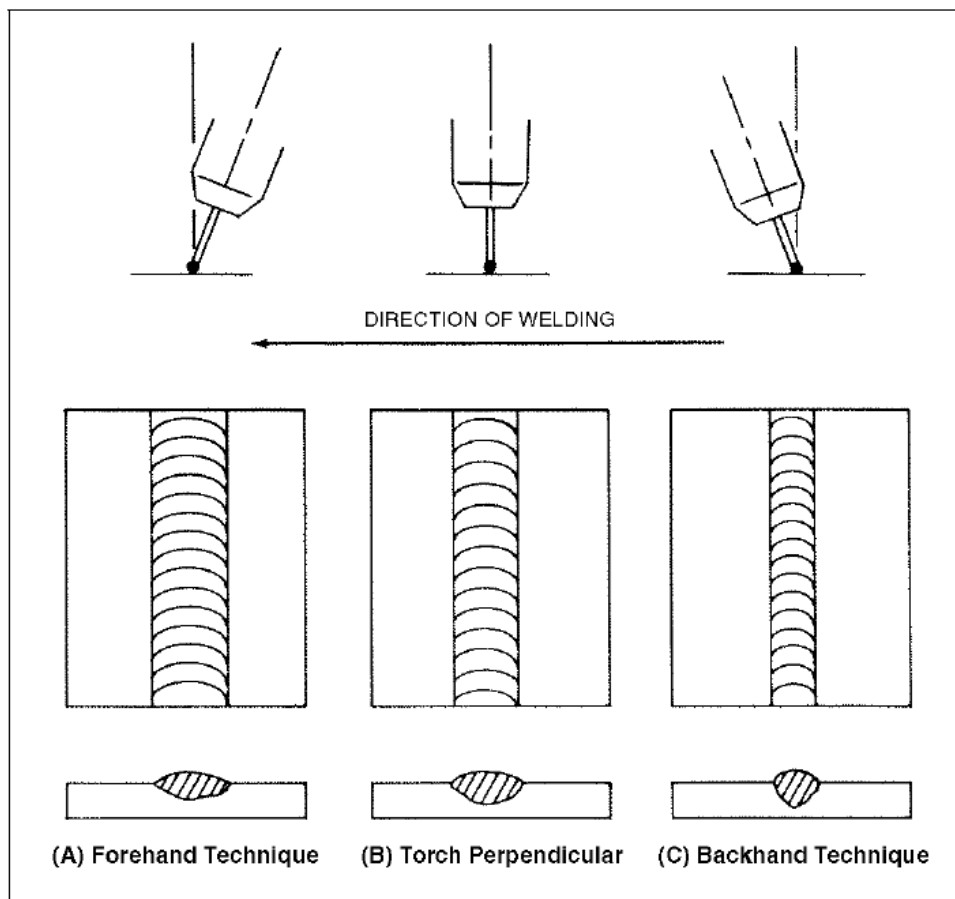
Efeito da orientação da tocha no cordão de soldadura para o sentido empurrando (A), perpendicular (B) e puxando (C) (Adaptado de Brien [9]).
